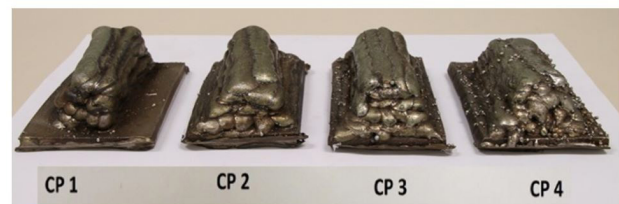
Esquema da confecção dos corpos de prova soldados através de processo de soldagem MIG/MAG.
